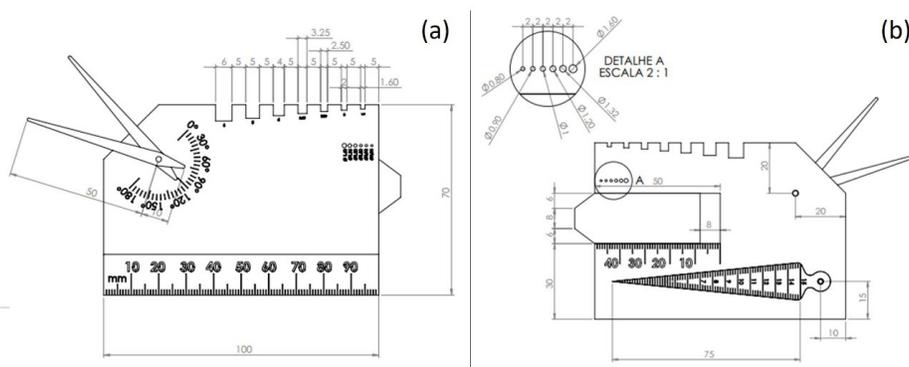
(a) - vista frontal do calibre de solda e (b) - Calibre de solda universal (CARBOGRAFITE, 2018)
